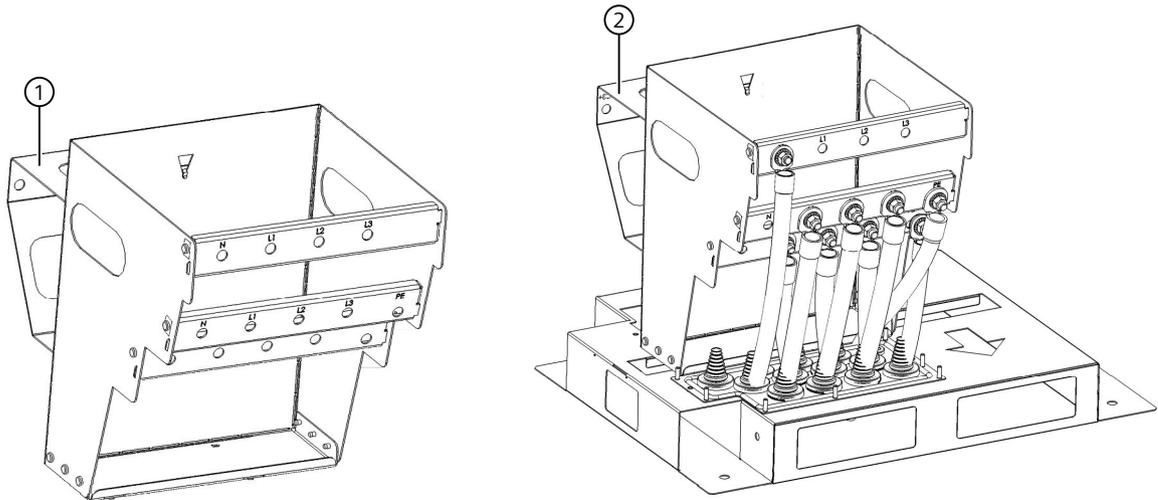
Bohrschablone und Kabeldurchführungsplatten
